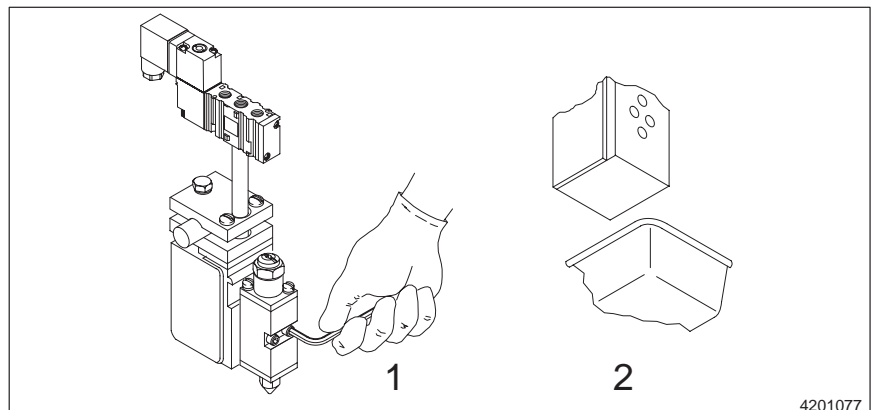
Dépose d'un module et mise en place d'un bac de récupération sous le corps du pistolet
